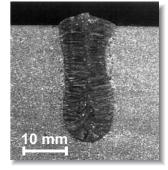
Beispiel extrem hoher Einschweißtiefe mittels Festkörperlaser.
